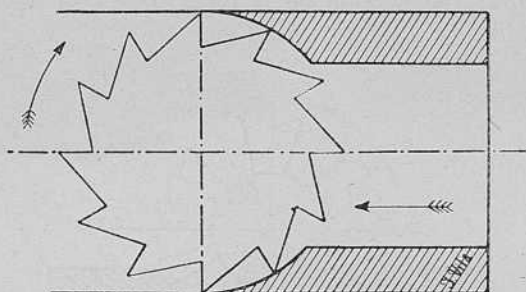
Trabajo de una fresa en el que puede ser mucha la profundidad de pasada, pero ligero el avance.
